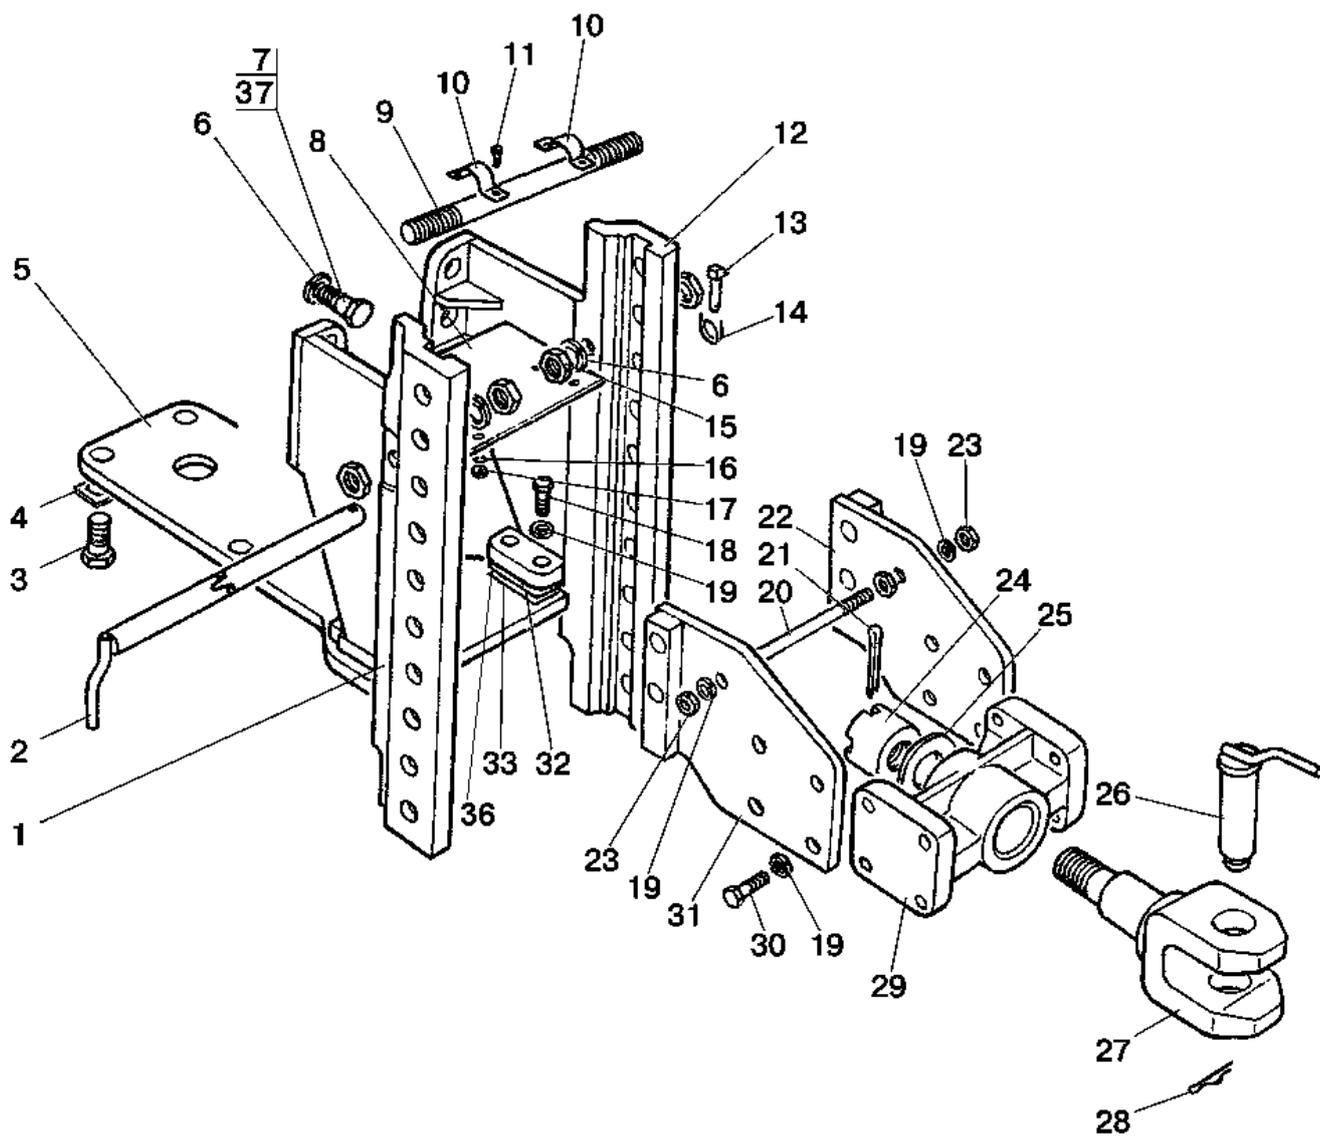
Тягово-цепное устройство (сварные боковины)
